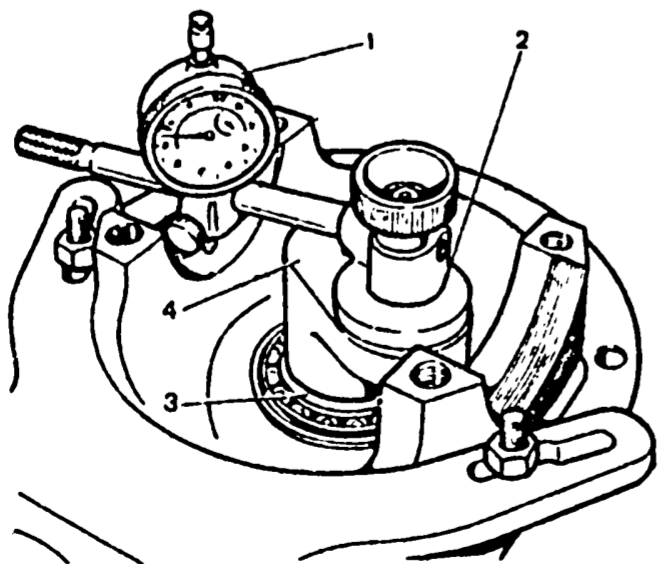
Определение толщины регулировочного кольца ведущей шестерни: 1 - индикатор; 2 - приспособление А.95690; 3 - задний подшипник ведущей шестерни; 4 - оправка А.70184
